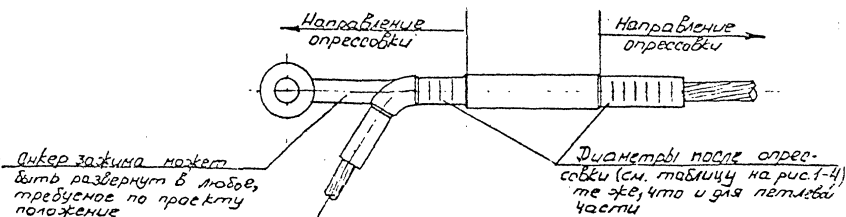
Опрессовка корпуса натяжного зажима НАСУС.
